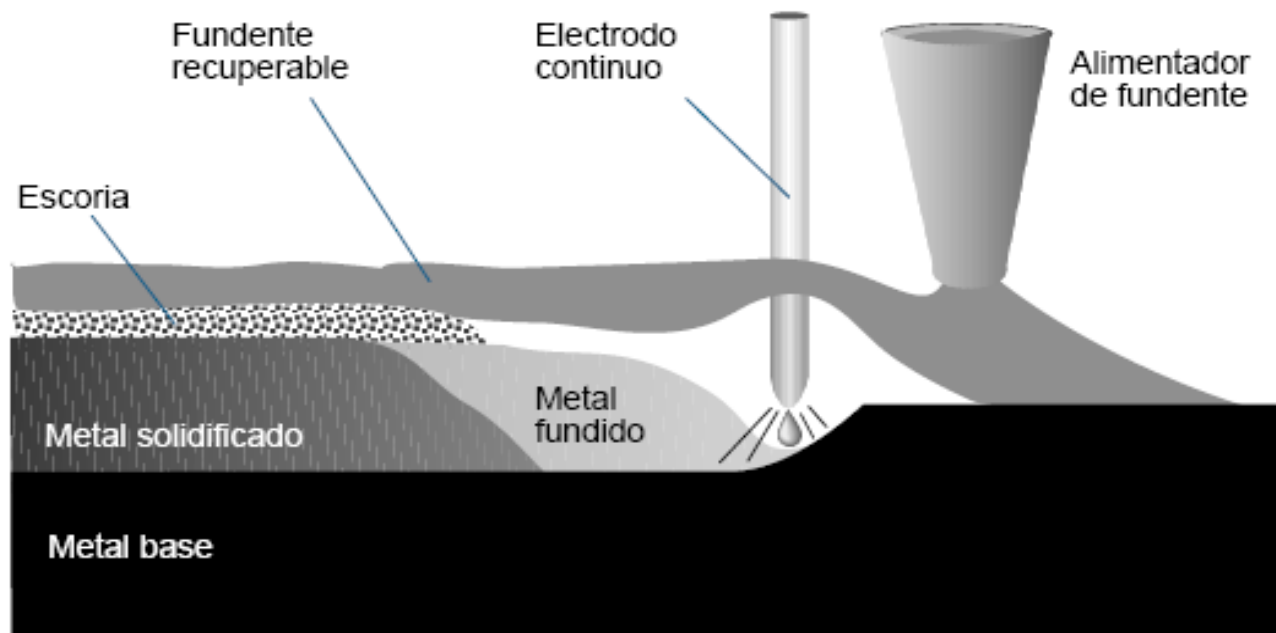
PROCESO DE SOLDADURA POR ARCO SUMERGIDO
